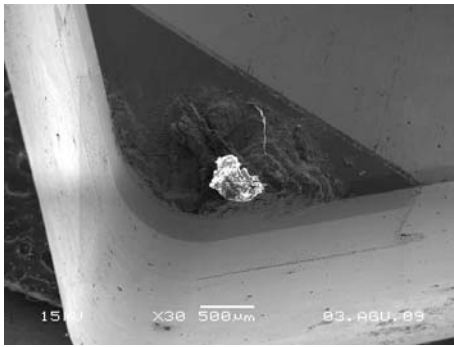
, 6.5 ve 6.6 incelendiğinde; %5 MgO kodlu numunenin işlenmesinde, üç kesici takımın uç kısmında, talaş yüzeyinde talaş yığılması (BUE) olduğu ancak en fazla yığılmanın KBN kesici takımında olduğu görülmektedir. Kesici uçlardaki aşınma davranışına bakıldığında, yan yüzey aşınmasının çok az olduğu, en fazla aşınmanın SK kesici takımında görüldüğü tespit edilmiştir. Bu durumu, kesici takım malzemesi olarak SK'nın KBN ve KBN K'ya göre daha düşük aşınma direncine atfedebiliriz.
